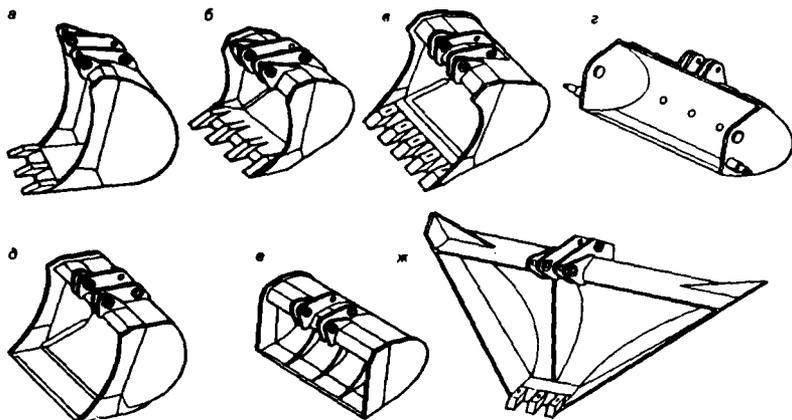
Ковши обратной лопаты гидрэкскаваторов 3-й размерной группы:
